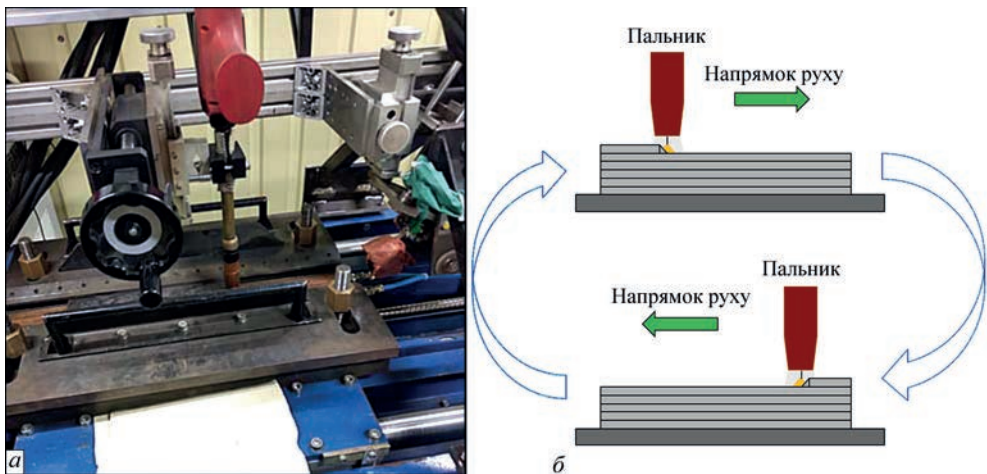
Обладнання та методика наплавлення: а – стэнд для наплавлення прямолінійних швів; б – напрямок руху пальника при пошаровому наплавленні
